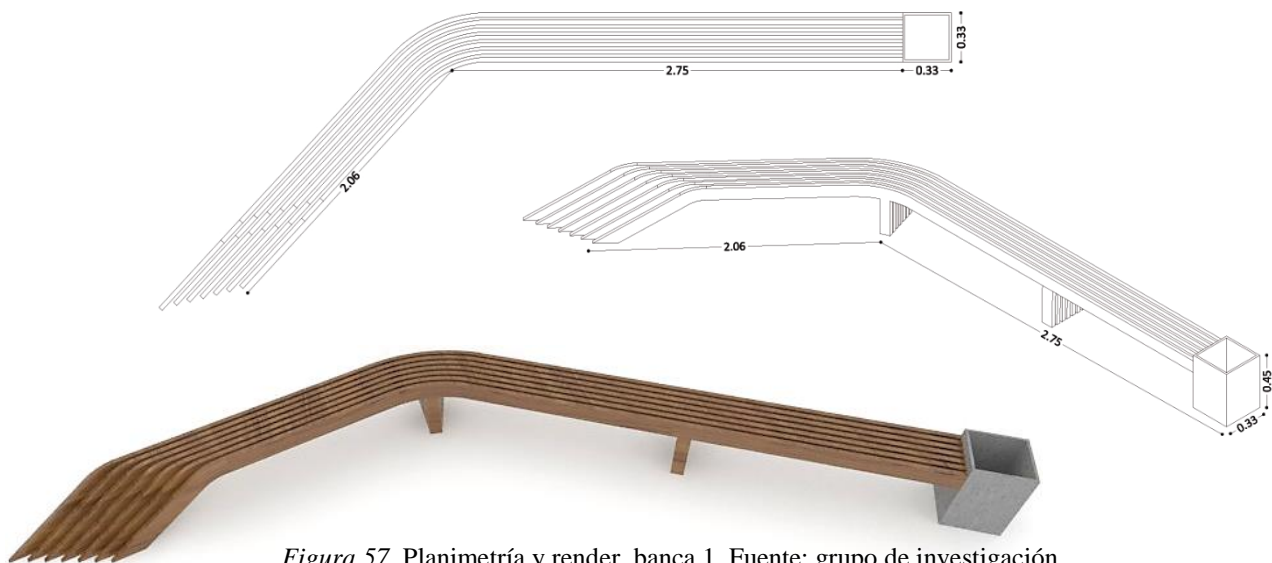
Planimetría y render, banca 1. Fuente: grupo de investigación.
